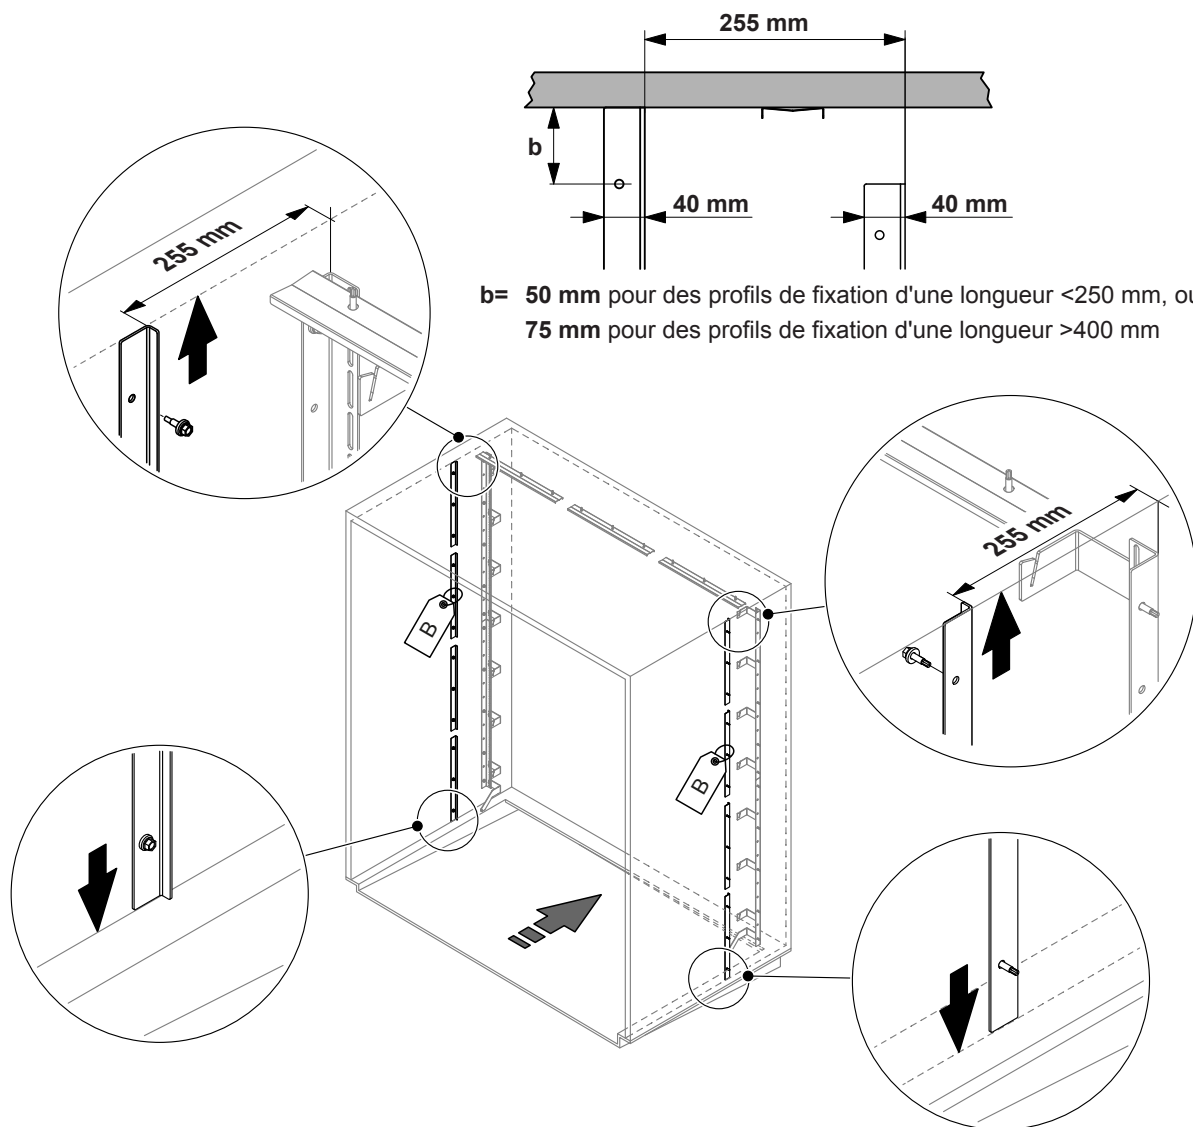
Montage des profils de fixation pour les tôles d'étanchéité latérales
